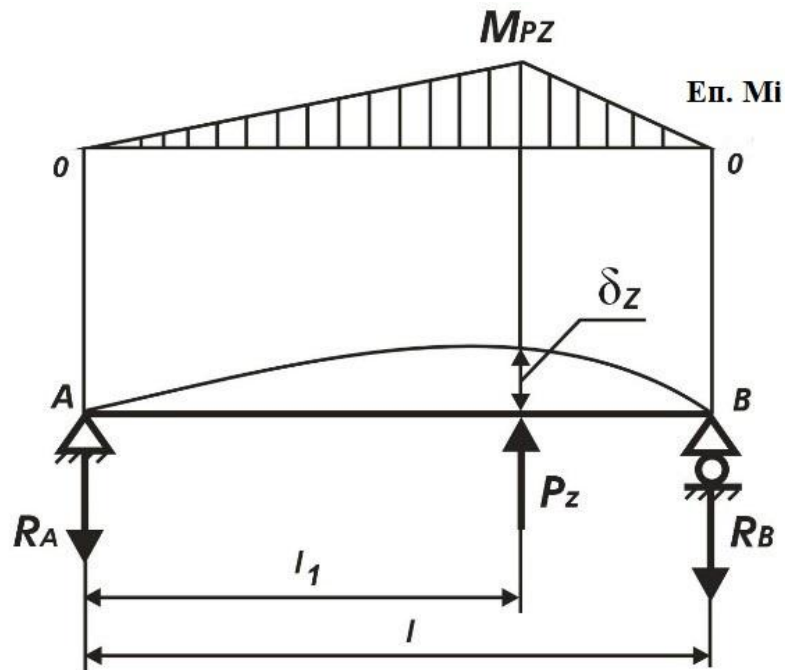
Схема навантаження колінчатого вала тангенціальною силою різання при механічній обробці
